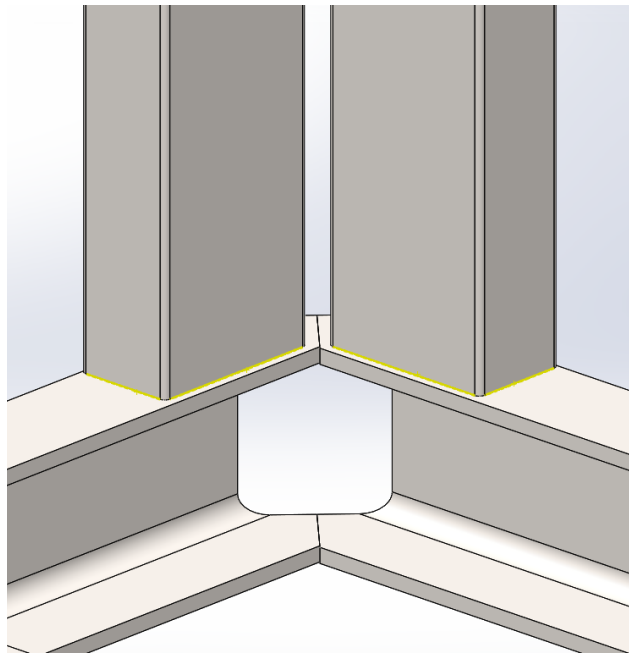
Detalles de soldadura de pilares delanteros
